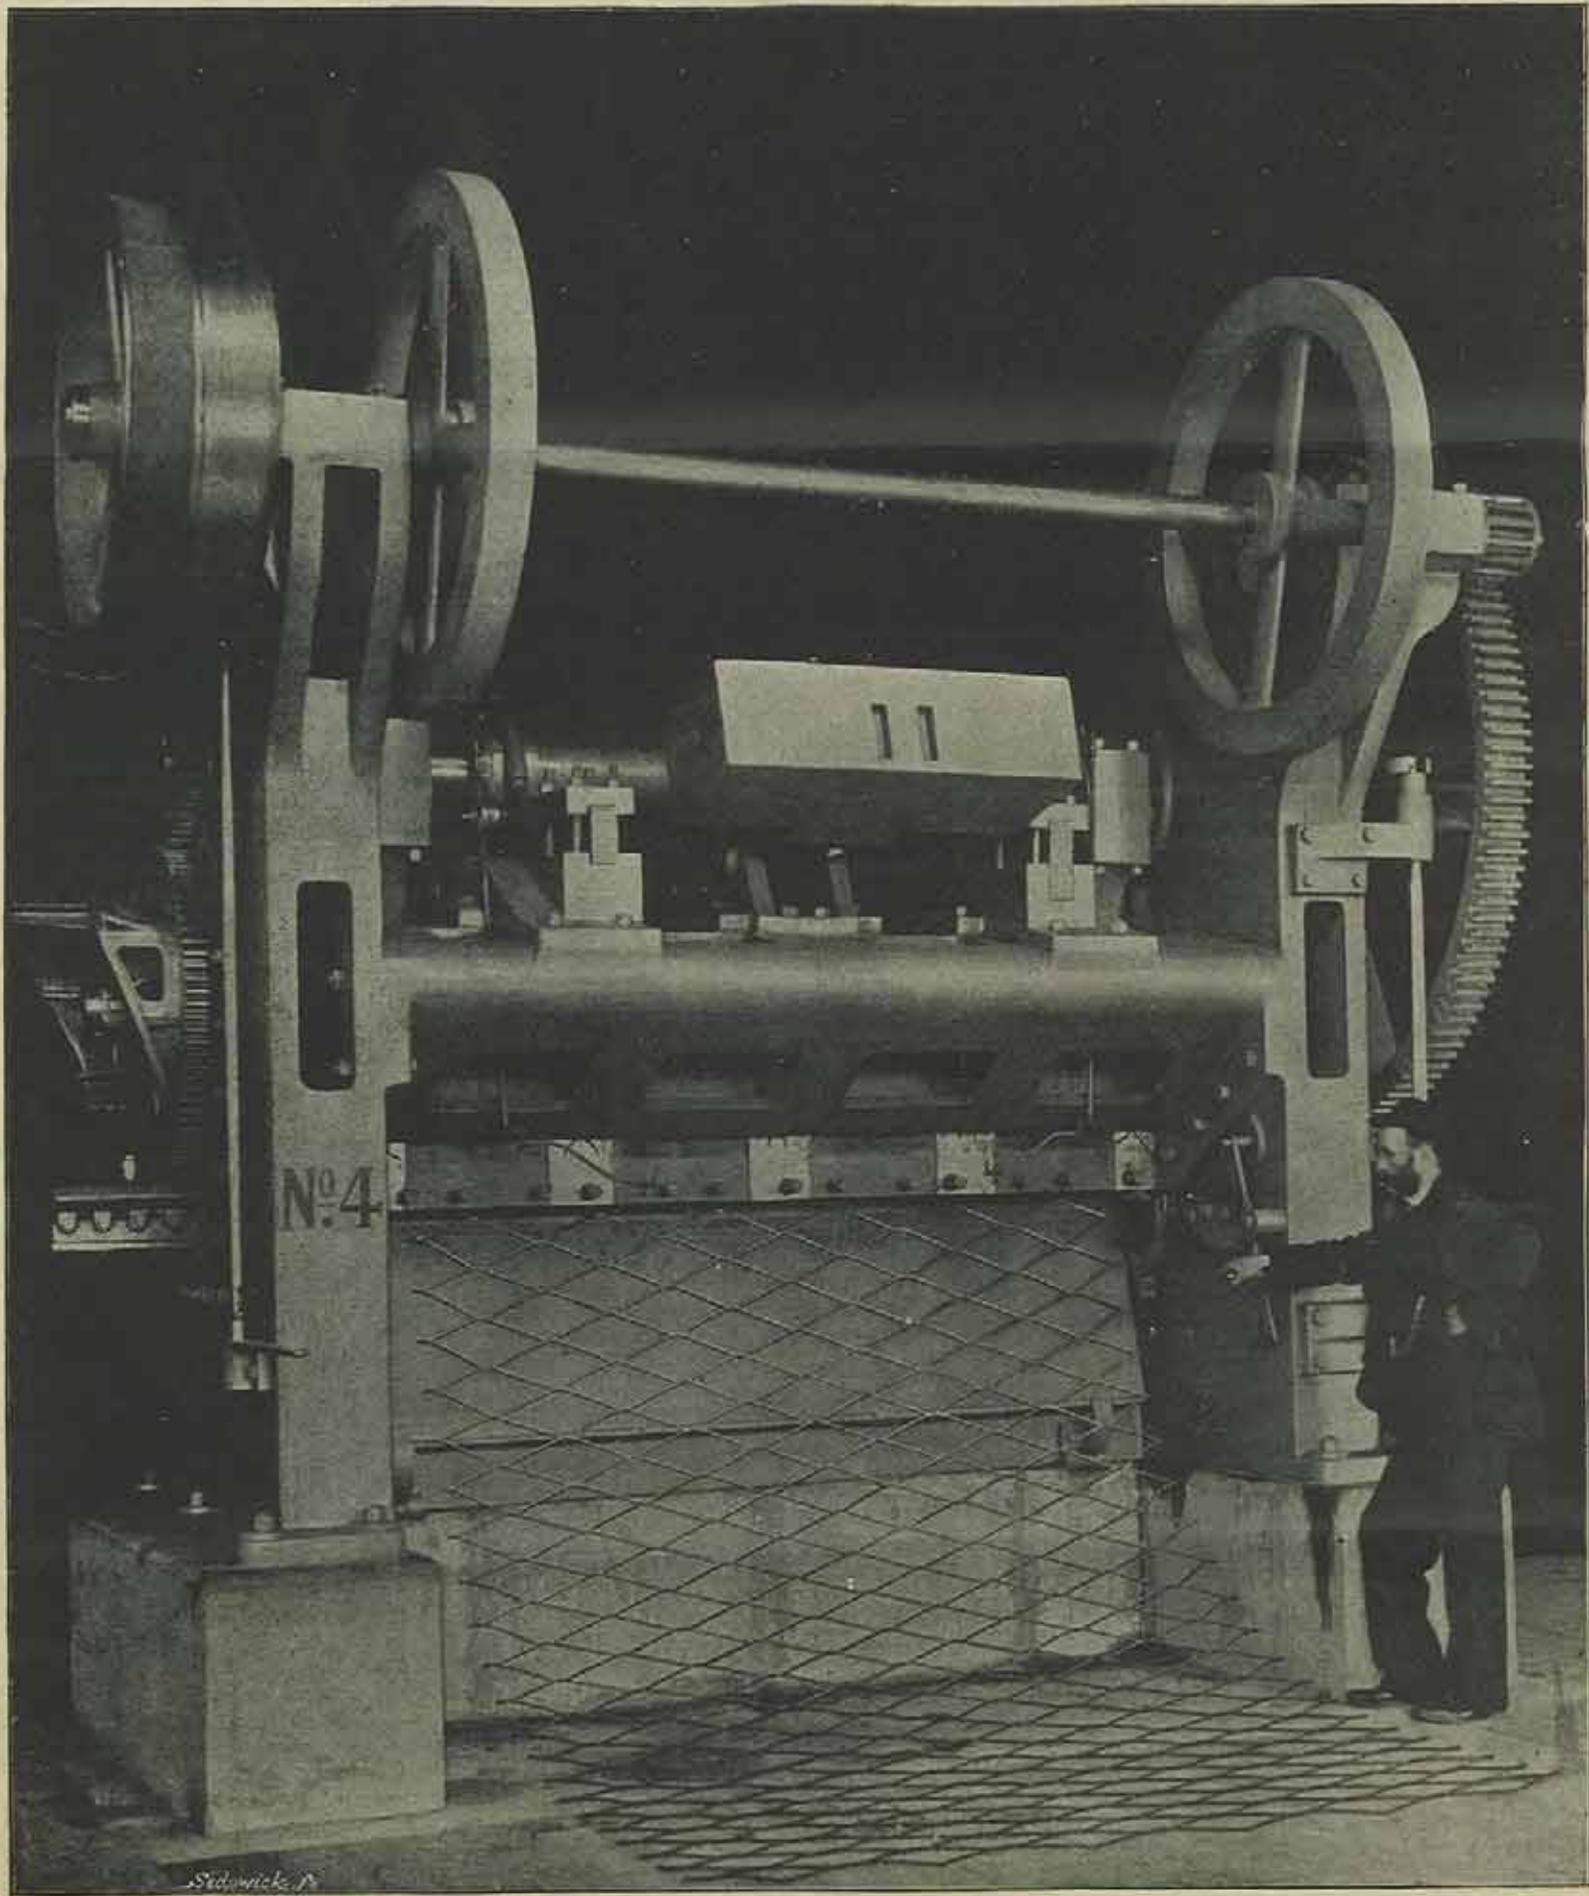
Machine pour la fabrication des treillis métalliques.
